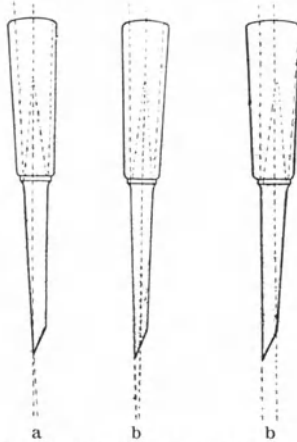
Befestigung der Klinge in dem Hefte der Stemmwerkzeuge.
